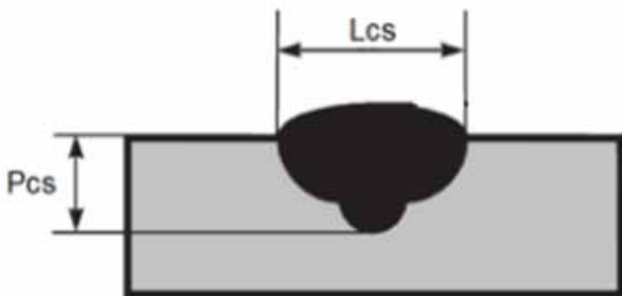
Parâmetros da geometria do cordão de solda avaliados. Pcs: penetração do cordão de solda e Lcs: largura do cordão de solda.
